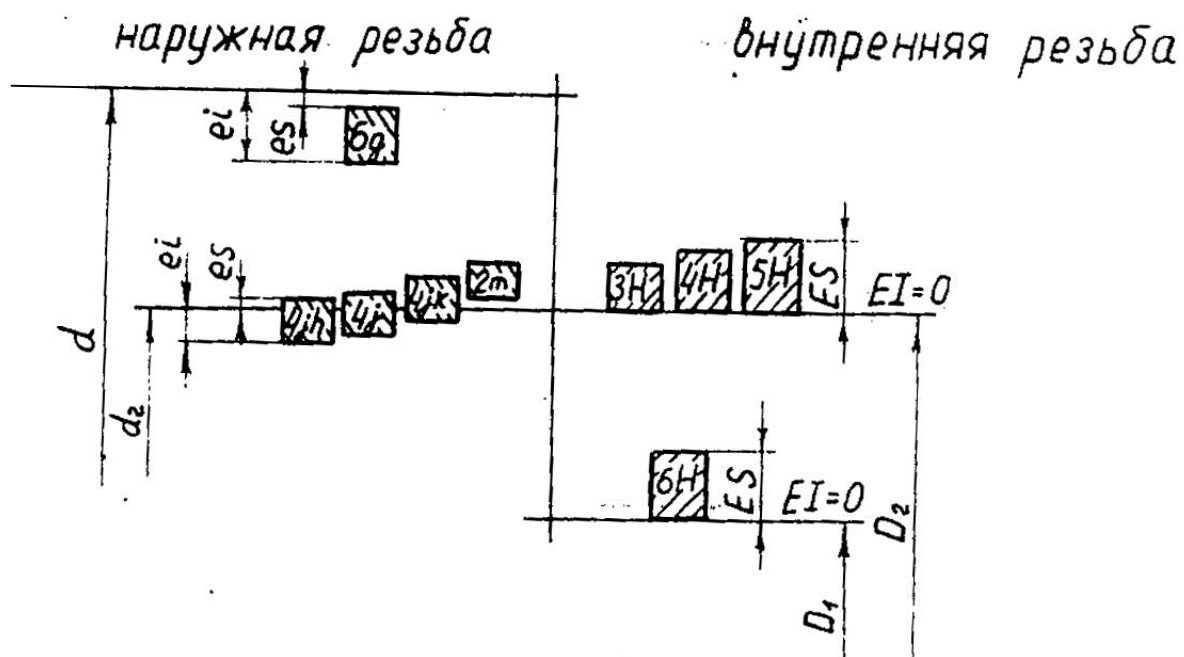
Схема расположения полей допусков резьбовых деталей с переходными посадками
